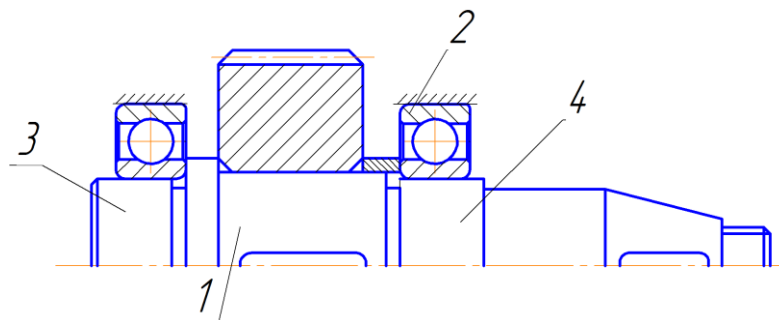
Прямой вал. 1 – вал, 2 – подшипники, 3 – шип, 4 – шейка.
